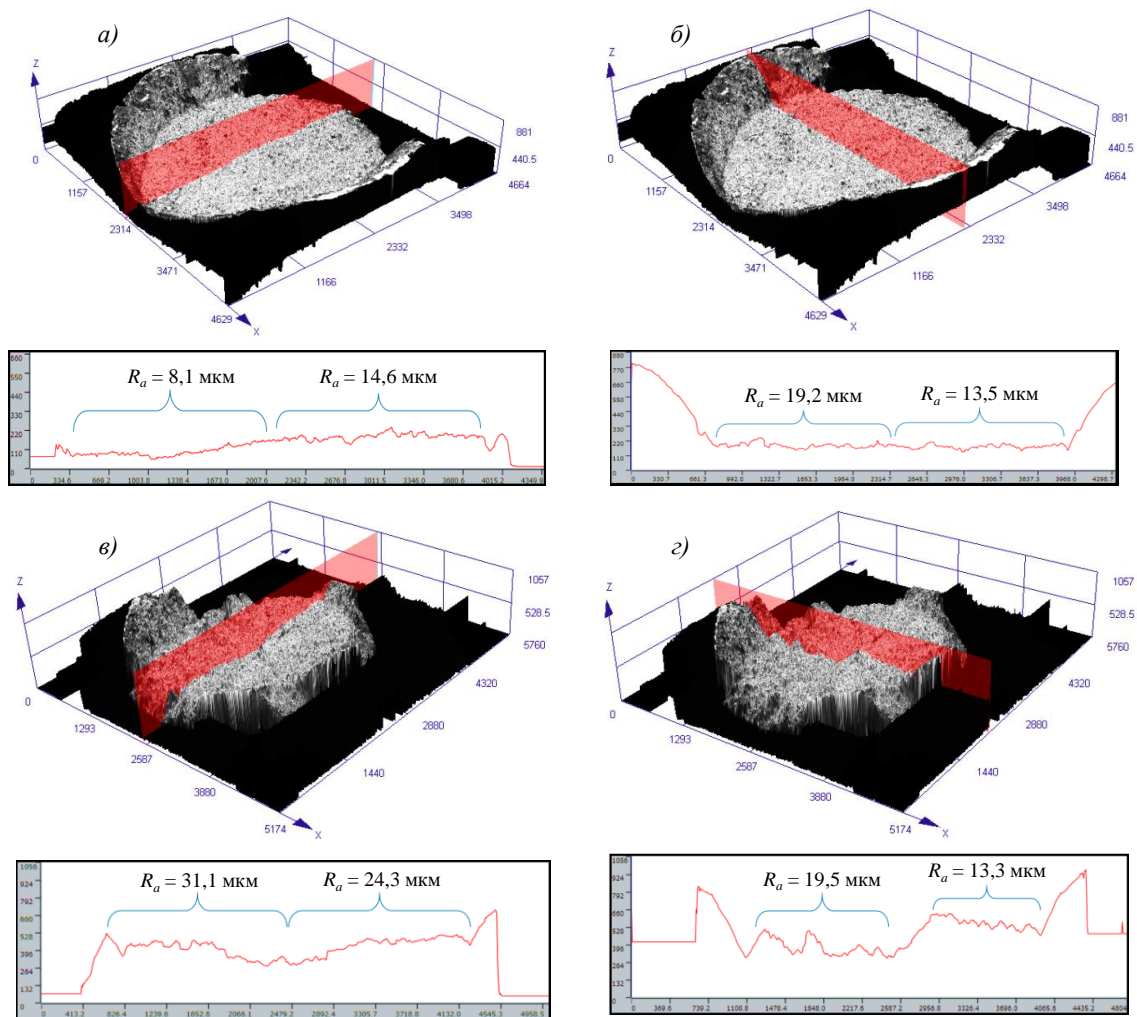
Общий вид и шероховатость поверхности разрушения аномального (а, б) и типичного (в, г) образца в сечении А (а, в) и Б (б, г)
